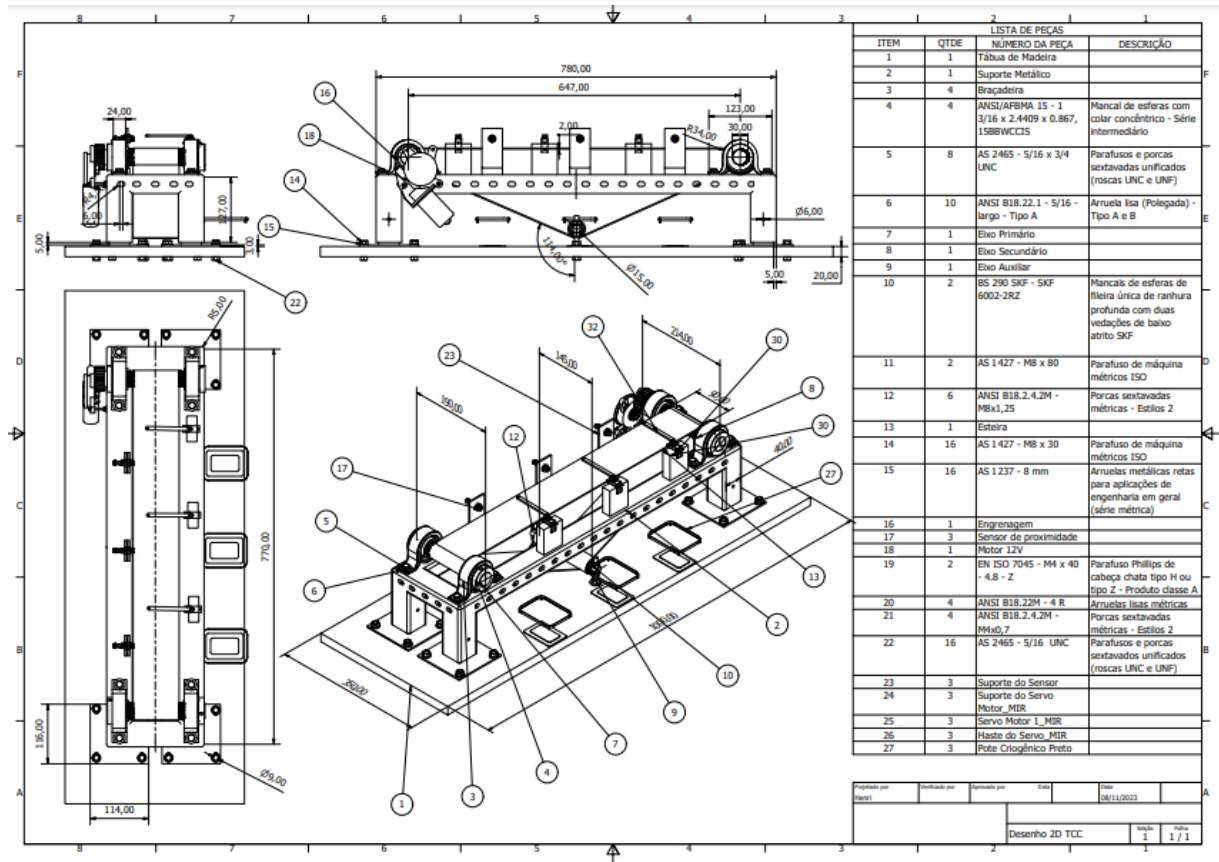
Desenho técnico final LixoTech – 3 vistas
